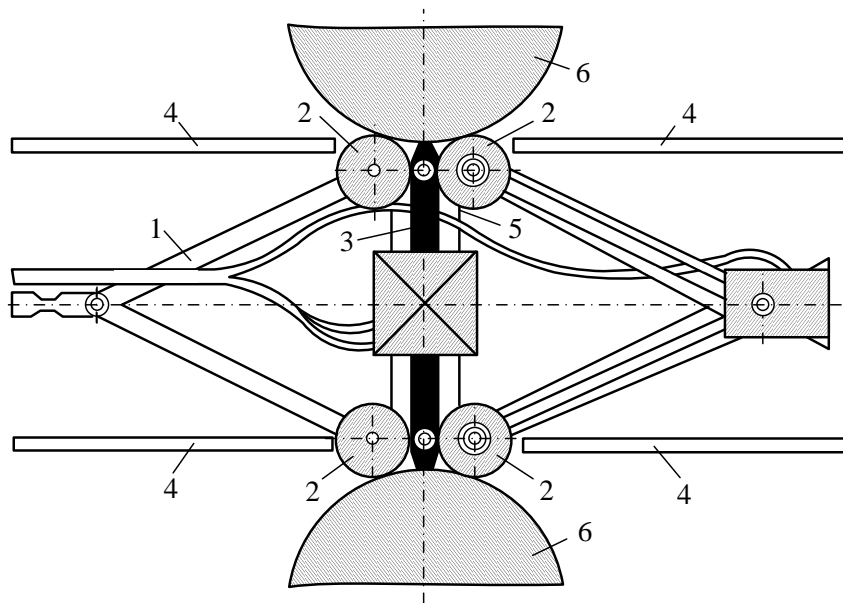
Устройство для контроля положения роликов: 1 – салазки; 2 – затравка; 3 – пружинный датчик; 4 – маятниковый динамометр; 5 – воздушный цилиндр; 6 – направляющие
